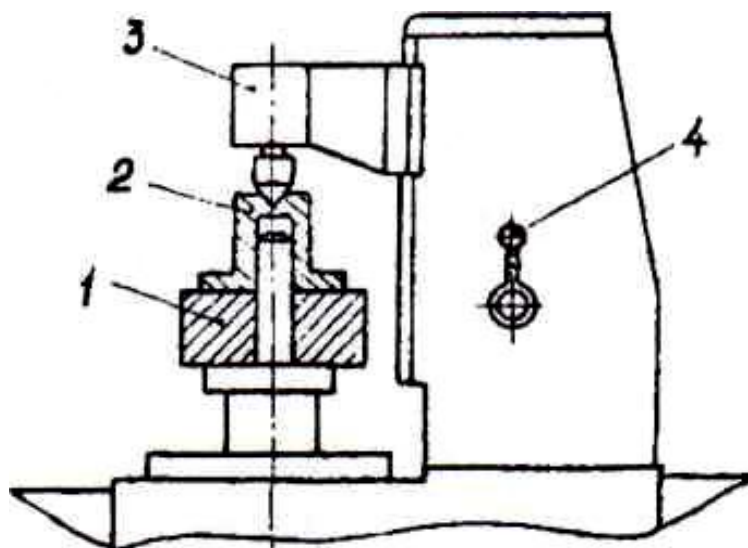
Схема встановлення та закріплення заготовки
